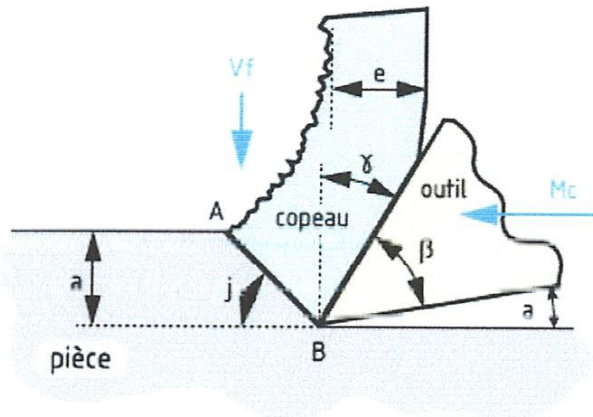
Exemple de coupe : usinage par enlèvement de la matière.
